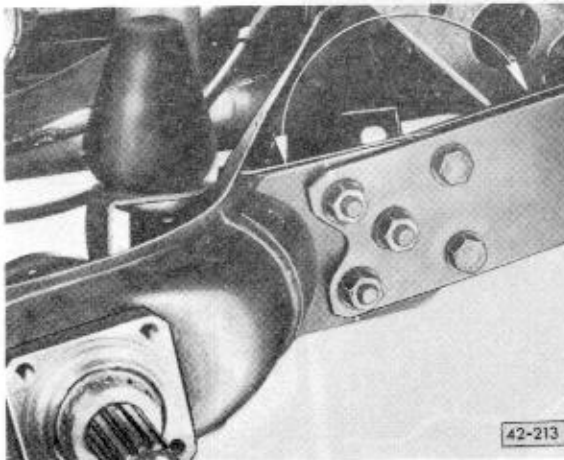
Einbaulage Federstrebe/Achsenkerflansch
